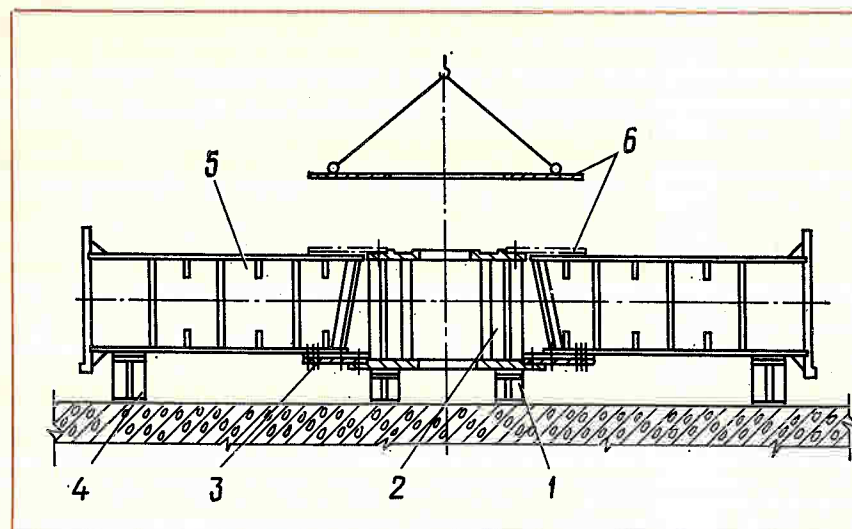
Сборка остова ротора гидрогенератора зонтичного типа
